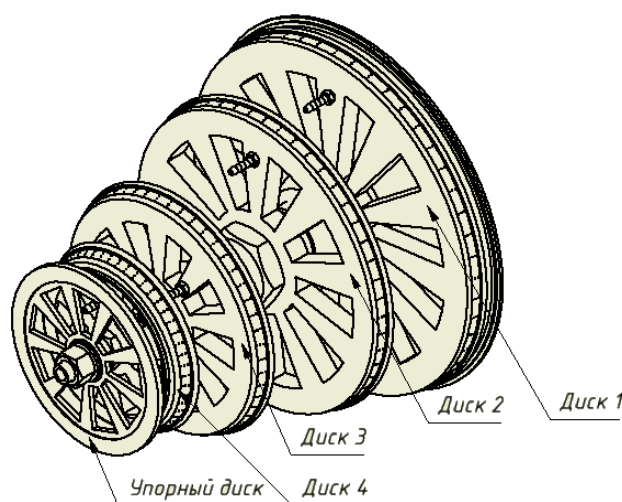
Предлагаемая сварочная оснастка. Вид общий
